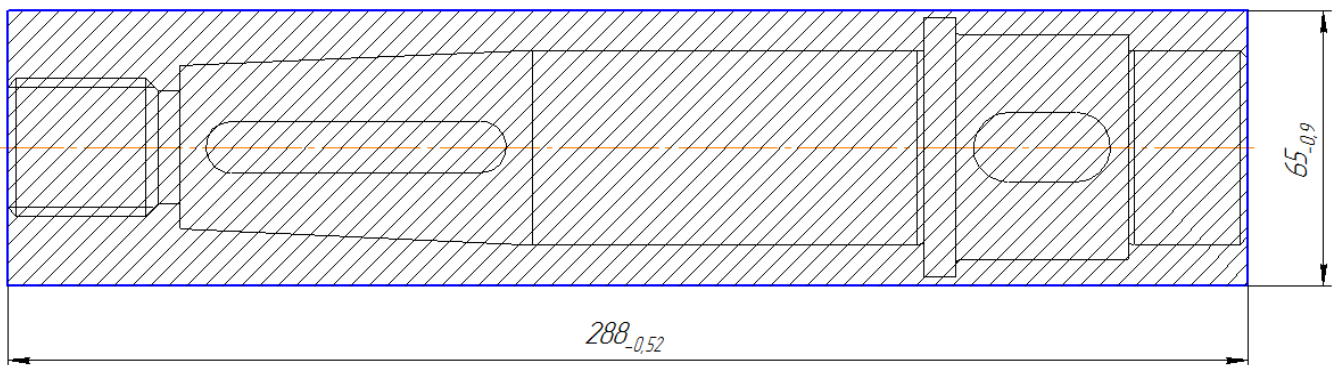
Ескіз заготовки - прокат розрізаний різцем
